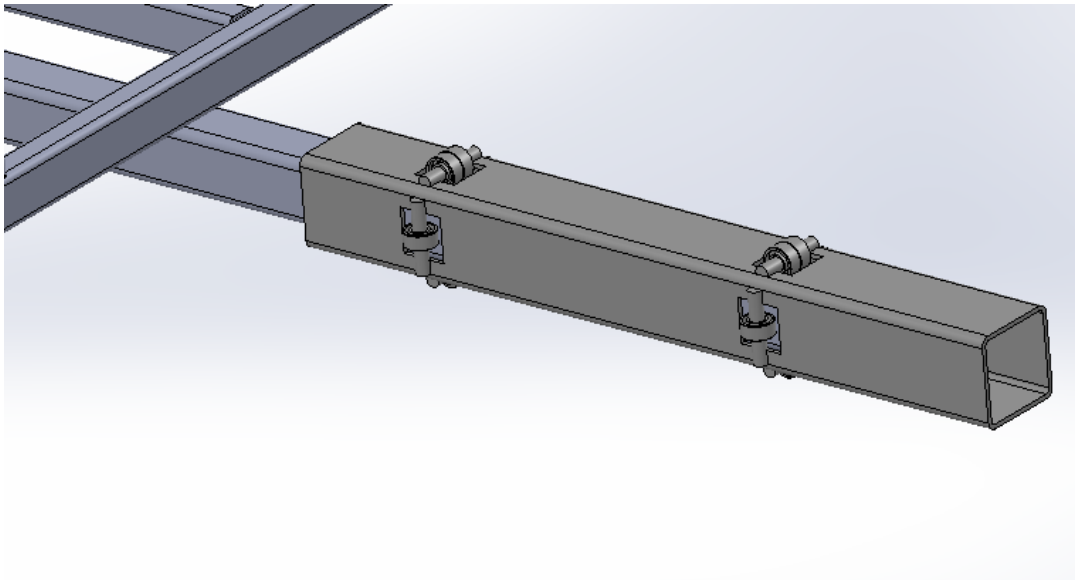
Tubo con rodamientos montado sobre estructura móvil
